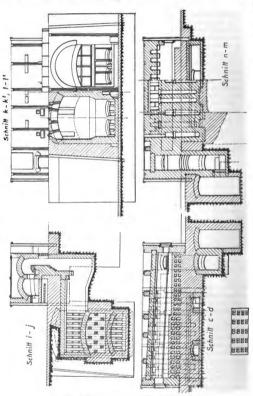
a. Rekuperator - Röhrenschweißofen.
